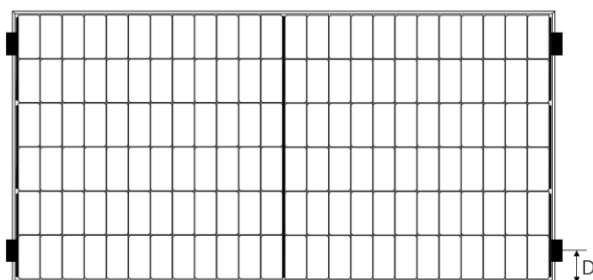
Montaggio di quattro morsetti sul lato corto del telaio
